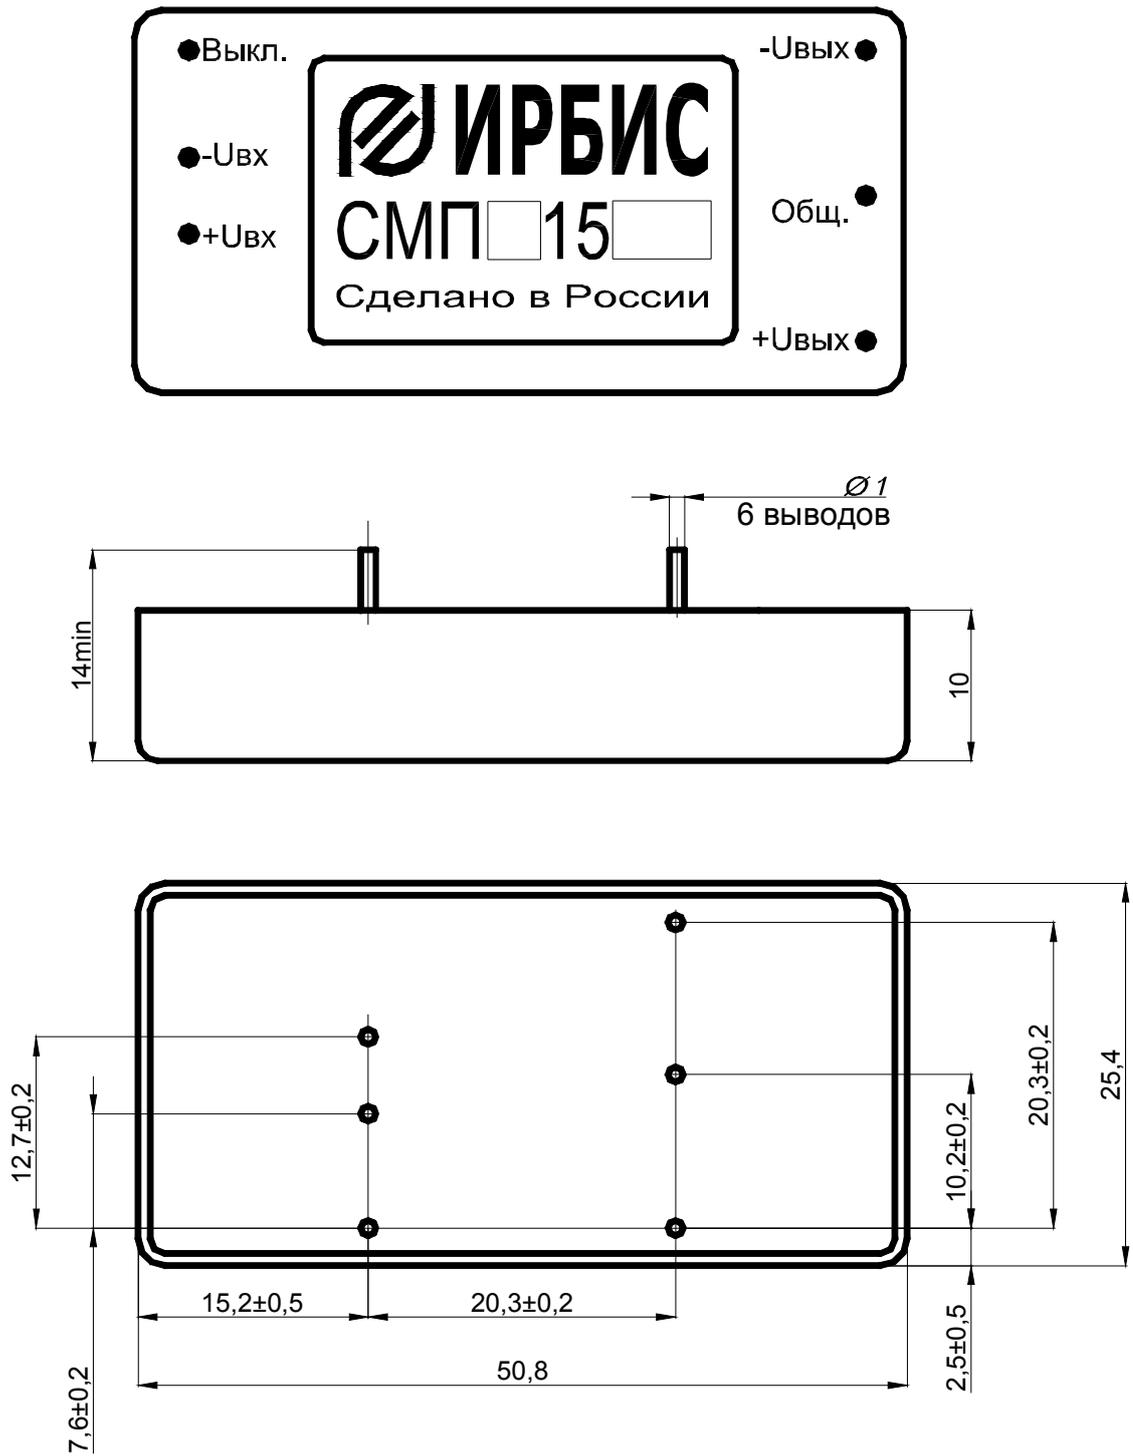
Габаритный чертеж модулей СМПА(В,Е,Т)15
